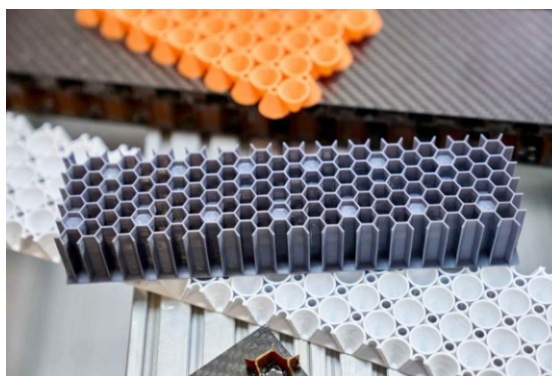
Звукопоглощающая конструкция с заполнителем различной высоты, полученная после снятия заготовки с матрицы
